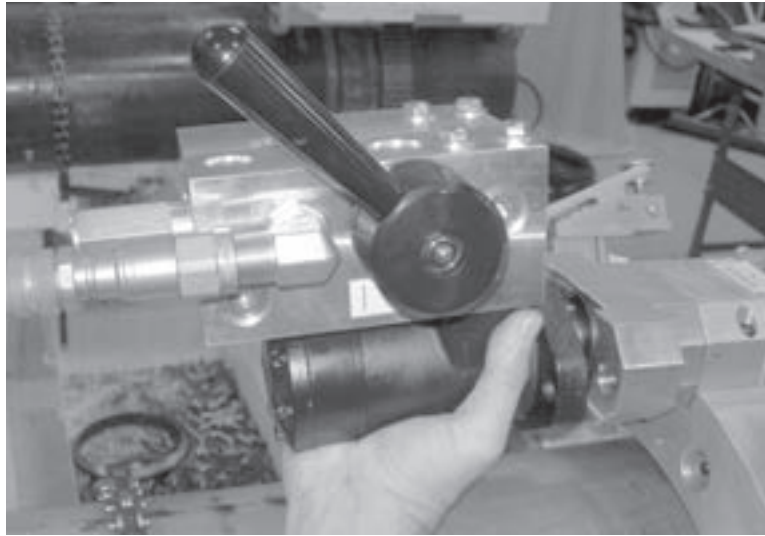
Inserte el eje de accionamiento hidráulico a través del adaptador de modo que el eje cuadrado encaje en el casquillo del piñón.
